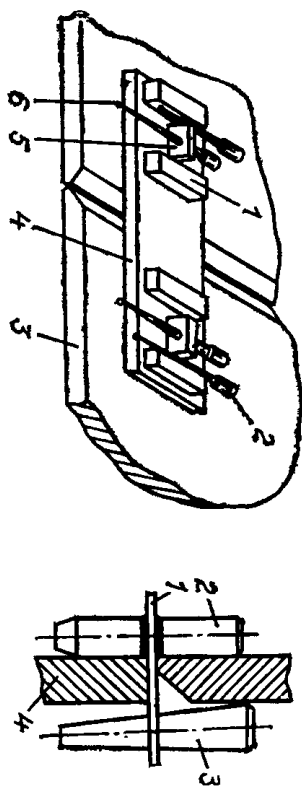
Полужесткое крепление стыка: 1 — брусок-упор; 2 — оправа; 3 — лист; 4 — сборочная планка; 5 — шайба; 6 — коническая оправа.
